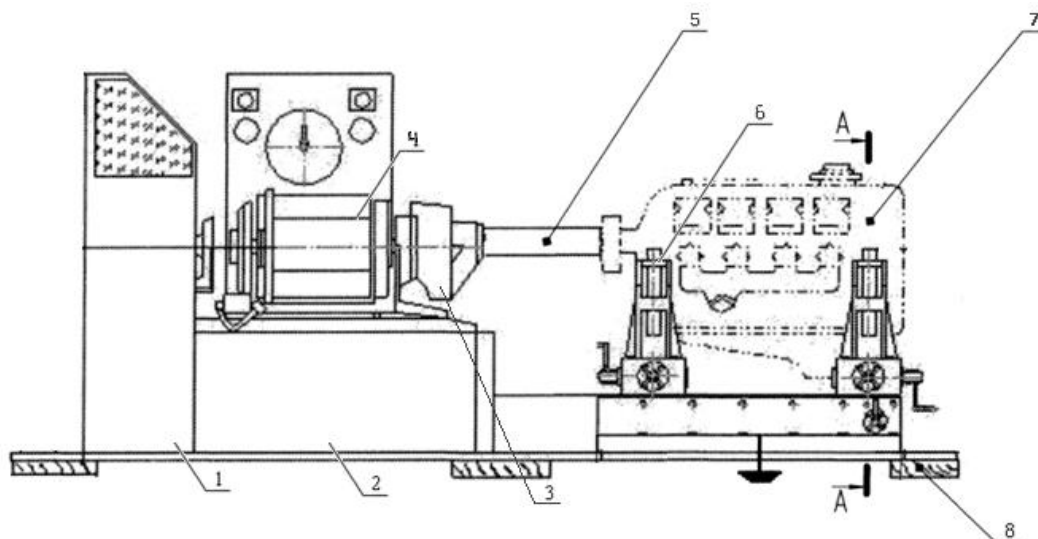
Схема обкаточно-тормозного стенда с планетарным редуктором: 1 – реостат; 2 – рама стенда; 3 – редуктор планетарный; 4 – электрическая машина стенда; 5 – вал карданный; 6 – стойка; 7 – двигатель обкатываемый; 8 – вибропоры стенда
